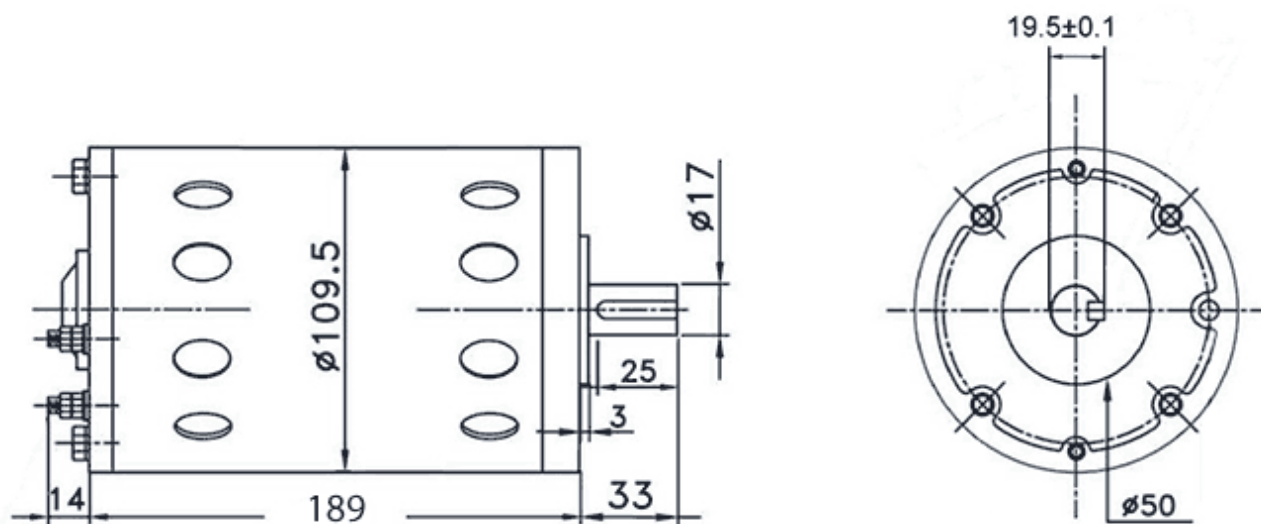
Габаритные размеры двигателя ДП500-24
